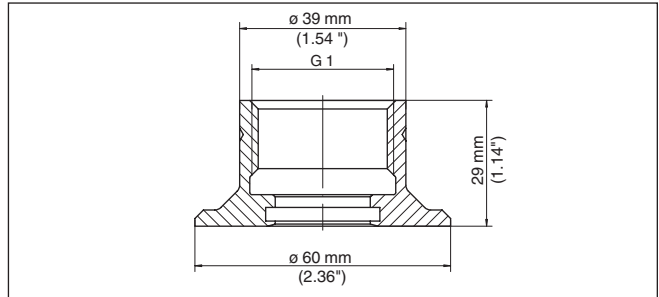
Dimensiones racor para soldar G1 (DIN 3852-A, ISO 228-1)
